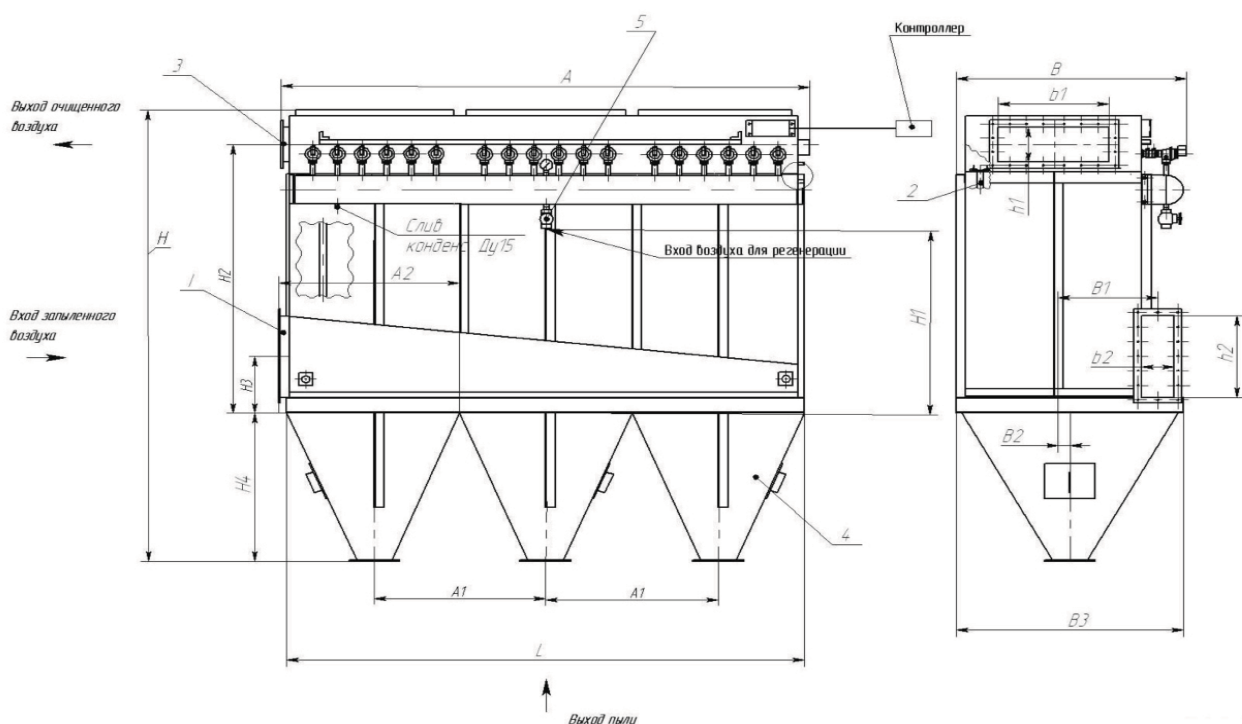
Схема фильтров рукавных типа FRIP-90; FRIP-540.
